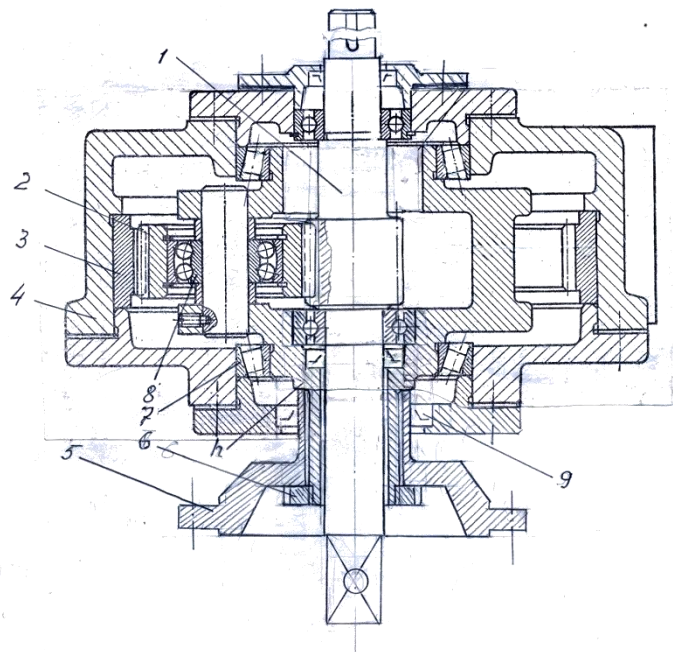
Конструктивна схема планетарного двохвального обертальника: 1 – центральний вал-шестерня; 2 – сателіти; 3 – нерухоме центральне колесо; h – водило; 4 – корпус; 5 – фланець вихідного вала; 6 – гайка; 7 – підшипник роликовий конічний; 8 – підшипник сферичний; 9 – ущільнення.
